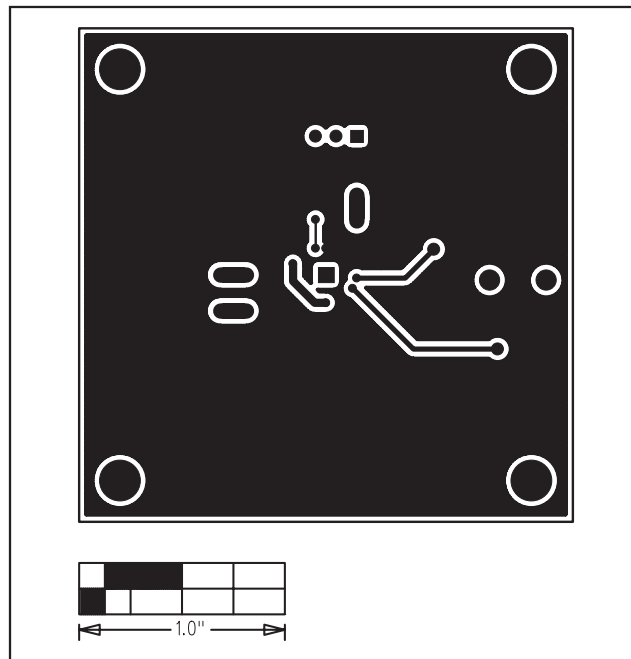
MAX9721 EV 키트 PCB 보드 레이아웃 — 납땜 측
